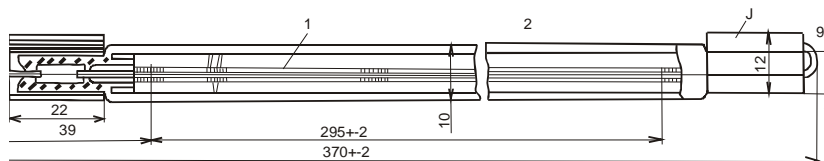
Схематичний розтин кварцового випромінювача КИ-1000:
